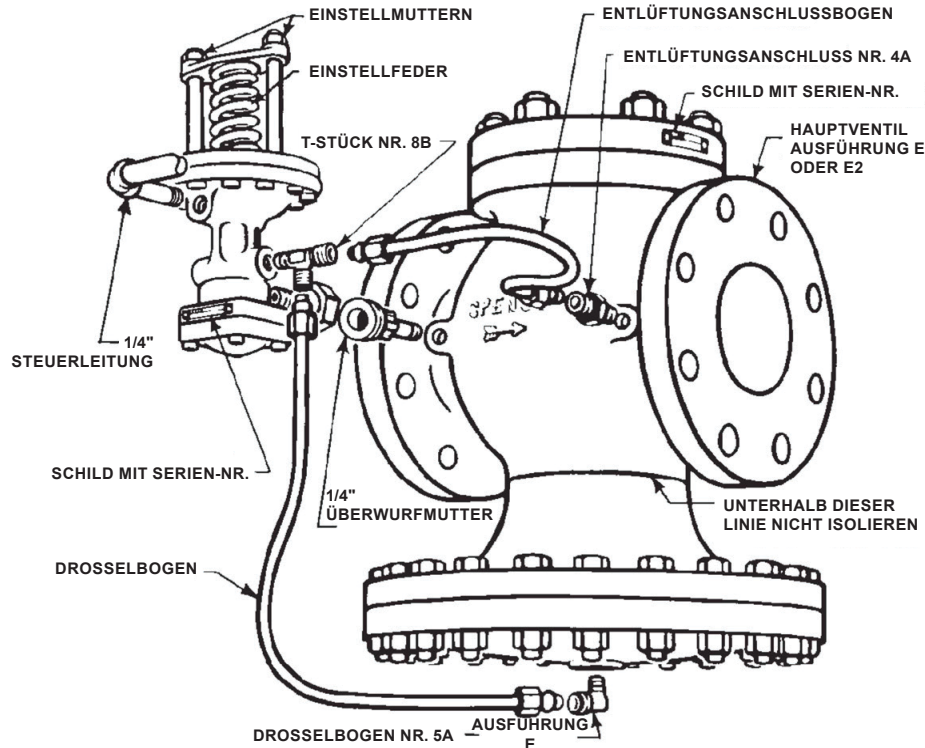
Montage des Steuerreglers an einem Hauptventil Ausführung E
